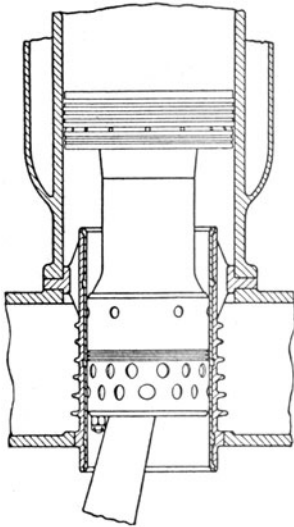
Kreuzkopfkolben mit Zylinder und Führung.
